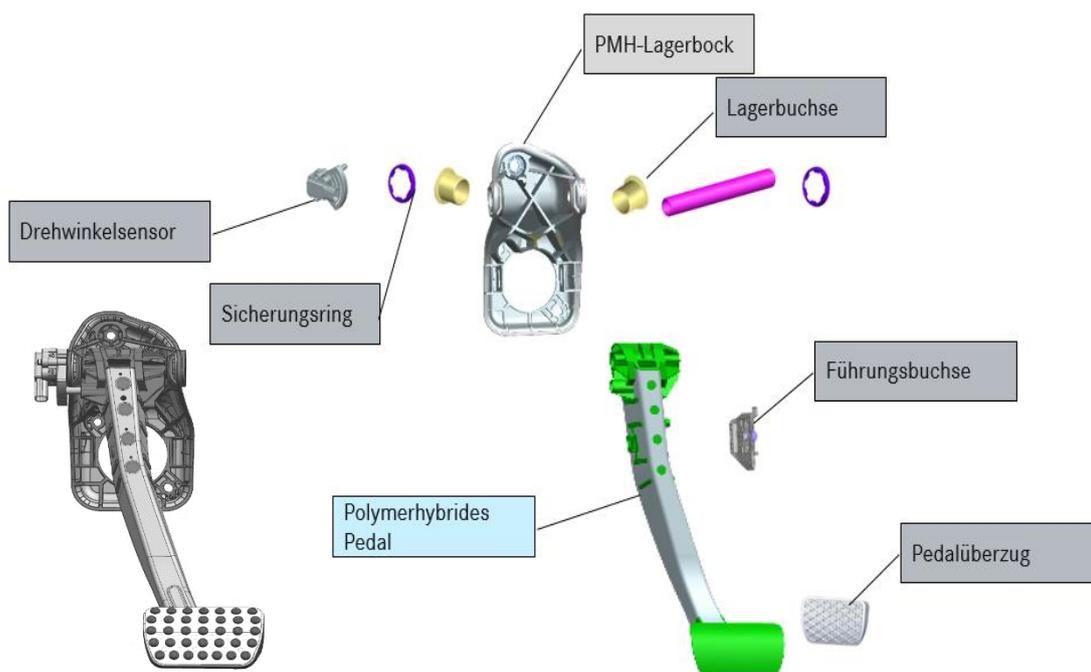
Explosionsansicht der MRA2 Bremspedalanlage
